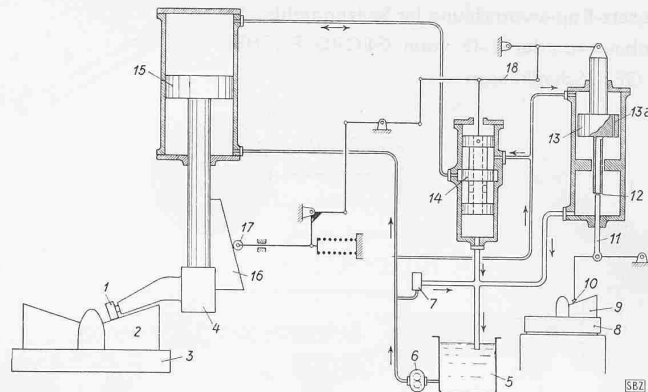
Prinzipschema der Kopiervorrichtung. 1 Fräser, 2 Arbeitsstück, 3 Arbeitsrundtisch, 4 Frässpindelkasten, 5 Oelbehälter, 6 Oelpumpe, 7 Abblaseventil, federbelastetes Ueberströmventil, 8 Modellrundtisch, 9 Kopiermodell, 10 Modellfühler, 11 Steuerstift, 12 Gesteuerter Abflussspalt, 13a Kopierservomotor, 13 Durchflussbohrung, 14 Steuerventil, 15 Hauptservomotor, 16 Rückführlineal, 17 Rückführrolle, 18 Steuergestänge
